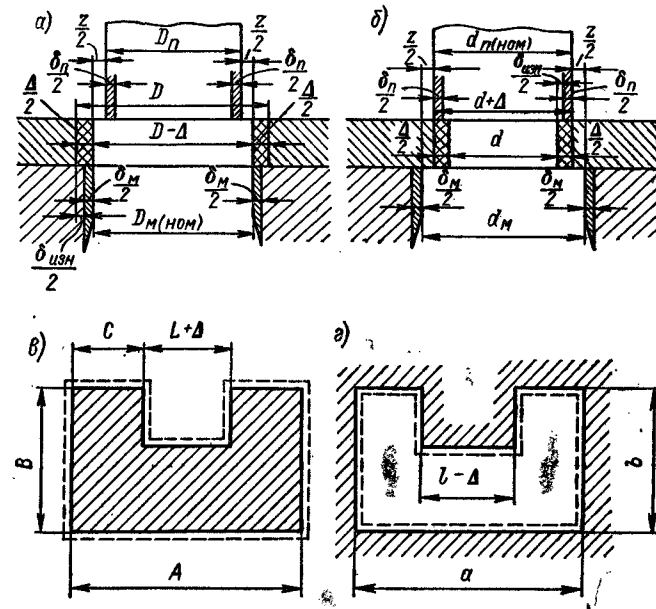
Схемы построения допусков на изготовление вырубных и пробивных пуансонов и матриц: а — при вырубке наружного контура; б — при пробивке отверстия; в, г — для увеличивающихся и уменьшающихся сопрягаемых размеров
